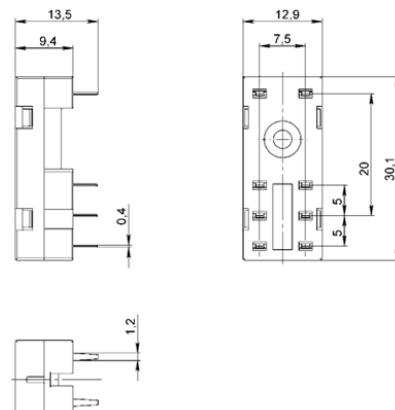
Габаритные, установочные и присоединительные размеры розеток OptiRel G RR95-12
